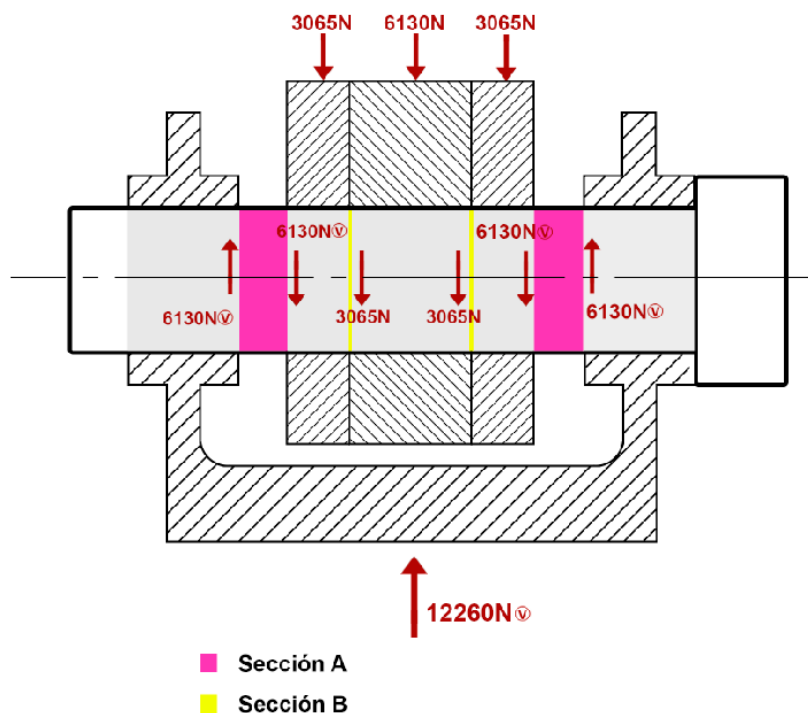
Actuator-Bancada. SECCION ALZADO
